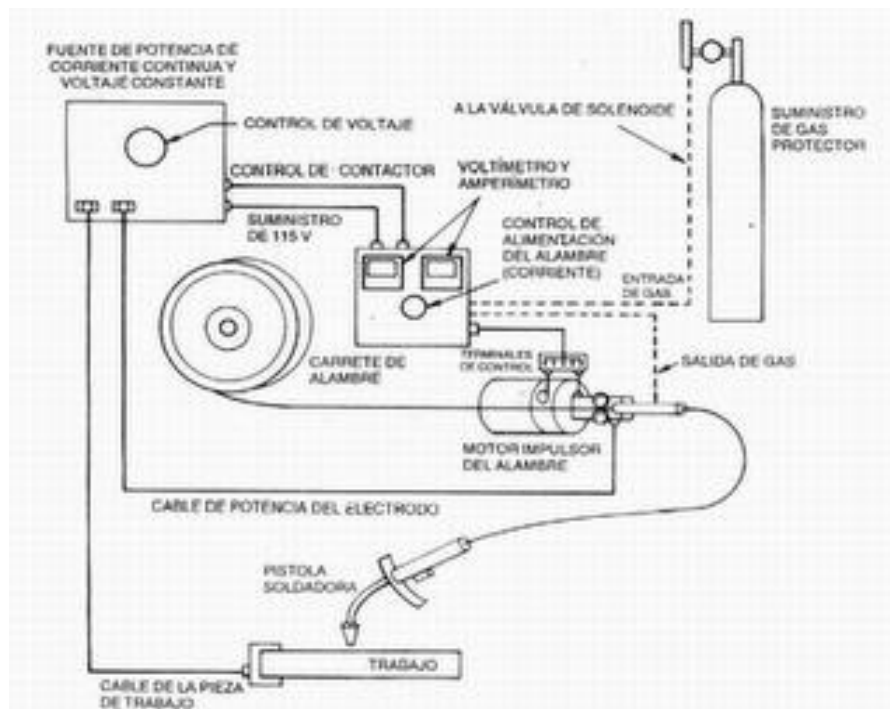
Esquema del equipo para la soldadura G.M.A.W.
